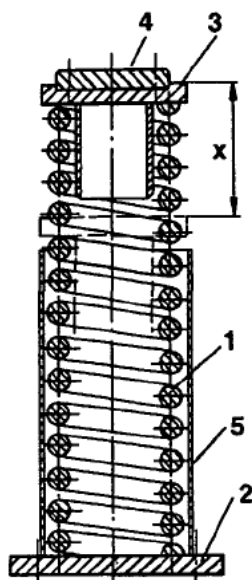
Пружинний буфер, 1 – пружина; 2 – нижня опорна плита; 3 – верхня опорна плита; 4 – гумова прокладка; 5 – циліндр.
